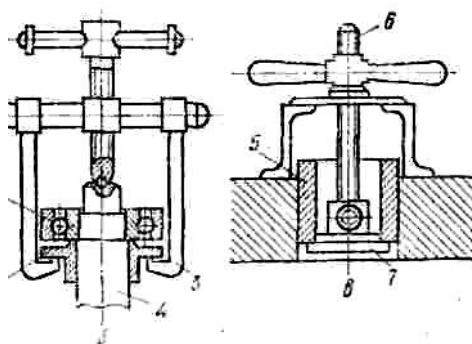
Приспособления для снятия шкивов, подшипников качения и скольжения.
